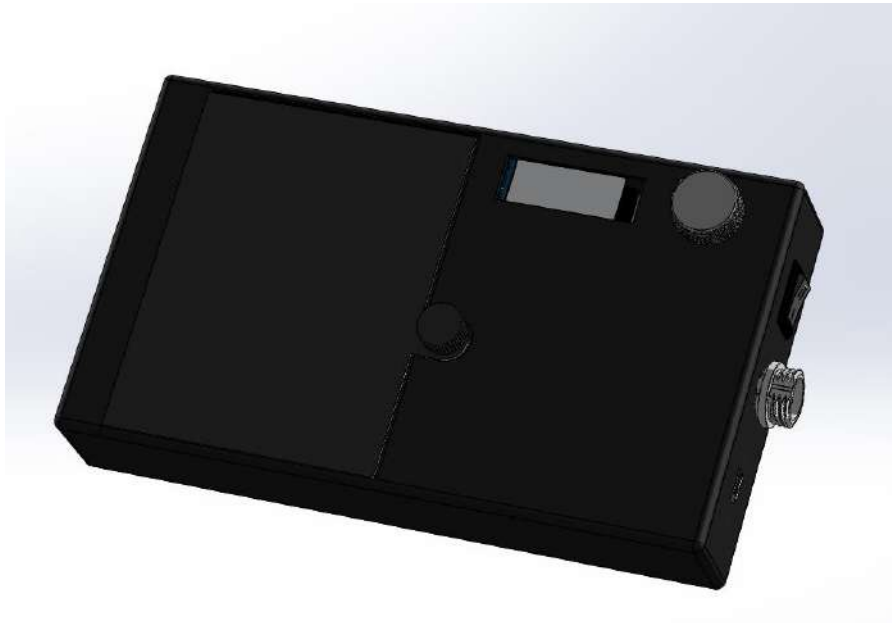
Верхня частина корпусу з кришкою для АКБ
